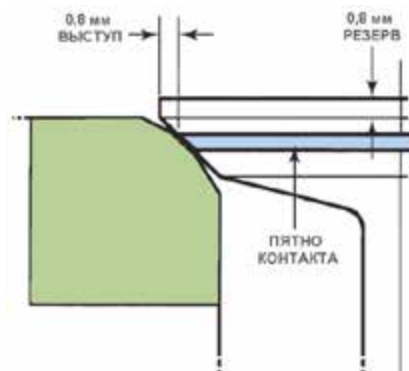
Пятно контакта должно равномерно располагаться по поверхности седла клапана и рабочей фаске клапана. При качественном обслуживании выступ и резерв клапана должны быть равны 0,8 мм; источник: *Pearson Education, Inc.
